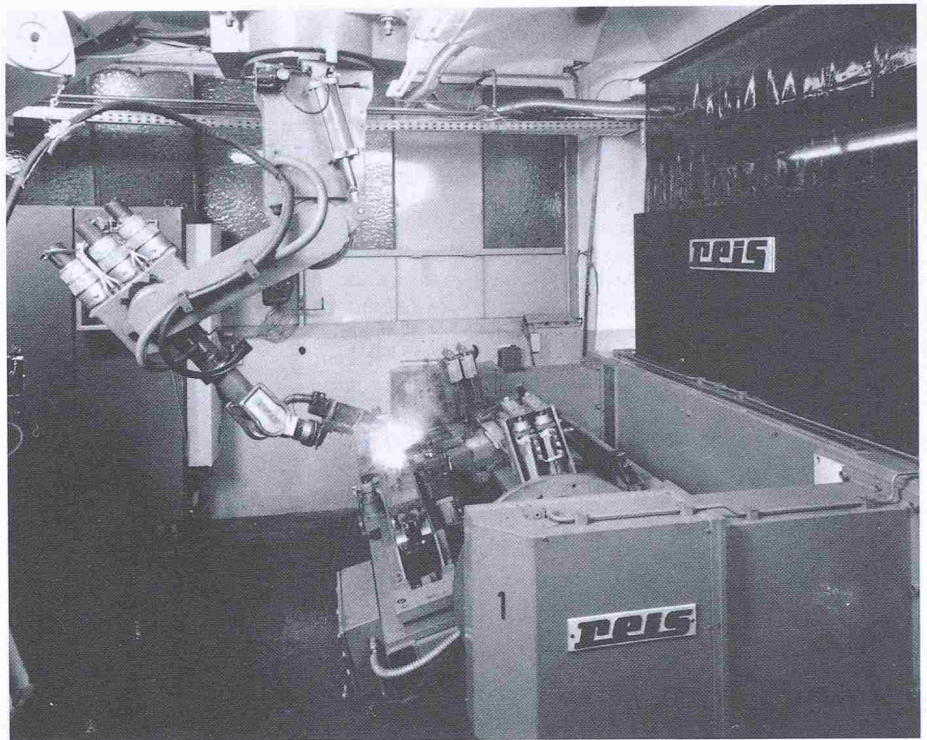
Roboterschweißen mit Zusatzachsentransformation
